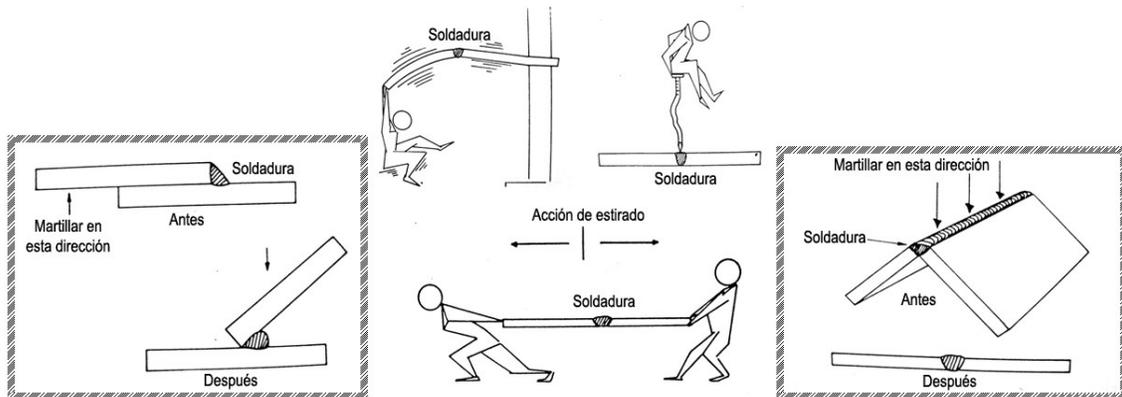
Se muestran las diferentes pruebas destructivas que pueden llevarse a cabo para saber si se realizó una buena aplicación en la soldadura. De izquierda a derecha tenemos en primer lugar una prueba en la que se martilla hasta lograr un doblado de 180 grados, en la figura central se presenta una prueba de flexión y tracción, por último a una unión en "V" se le martilla hasta dejarla en un plano horizontal.
